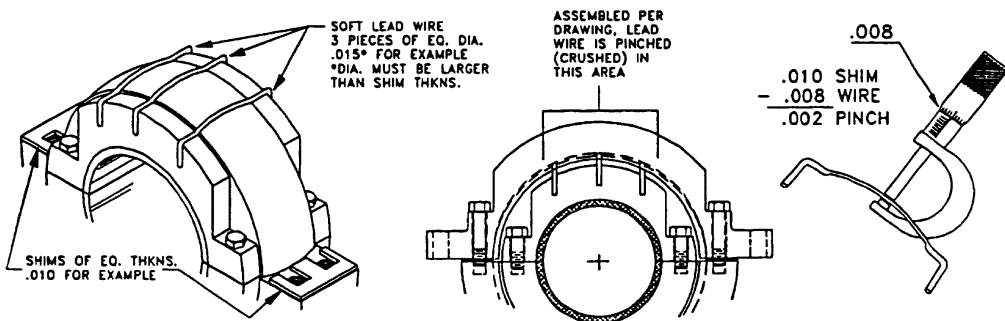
Ball Seat 저널 베어링의 Pinch Check
